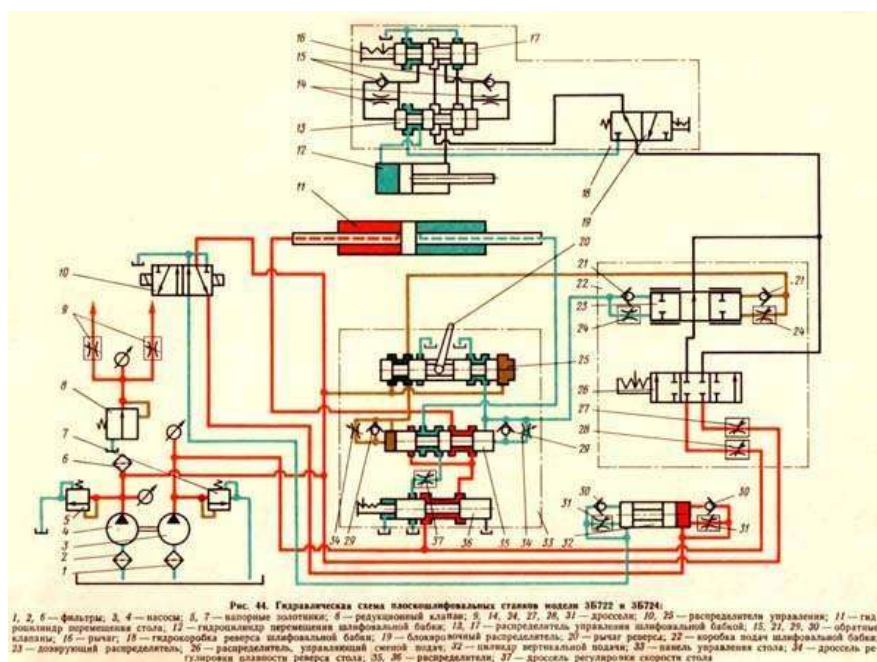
Схема гидравлическая плоскошлифовального станка 3Б722
